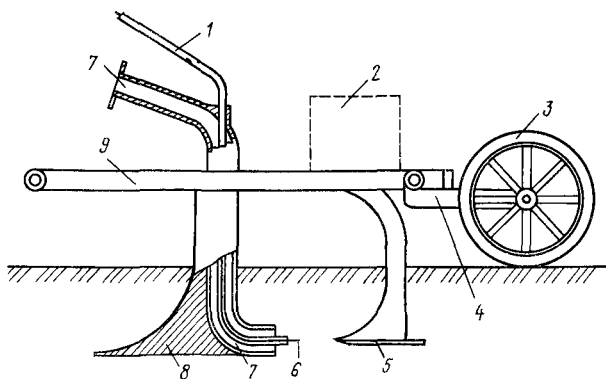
Электрогидравлический плуг для сухой почвы. 1 — токопровод, 2 — высеивающее или посадочное устройство, 3 — опорные колеса, 4 — кронштейн для подъема колеса, 5 — пластина заднего иожа (отрицательный полюс тока); 6 — положительный полюс тока, 7 — трубопровод для подачи воды или жидкого удобрения, 8 — передний нож, 9 — плужная рама
